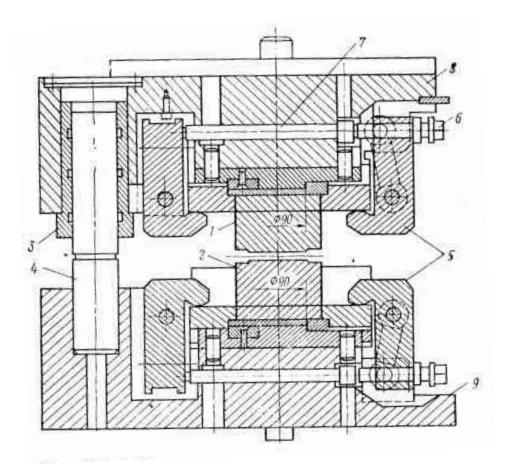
Схема конструкции штампа для штамповки поковок на кривошипном горячештамповочном прессе (гравюра на вставках 1 и 2 показана):
